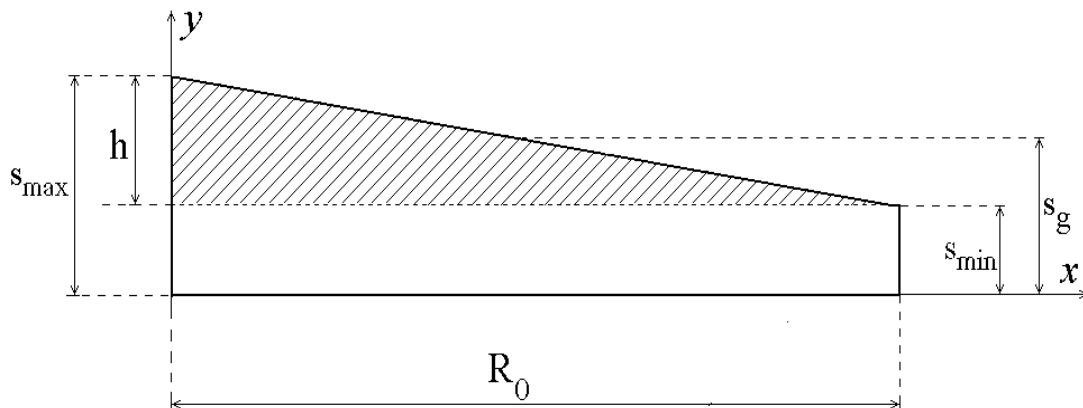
Расчетная схема формы коническо-цилиндрической заготовки
